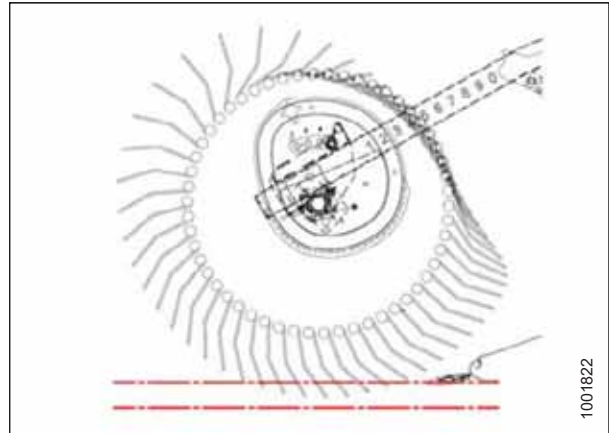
Вертикальний розріз пальця — положення 4
